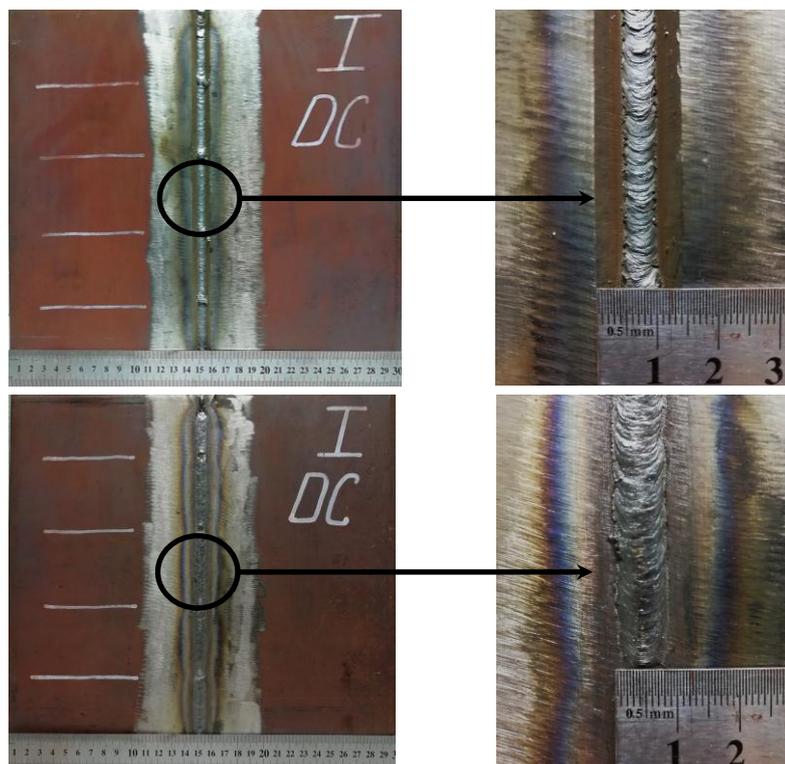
Лицевая сторона и обратный валик сварного соединения, выполненного на постоянном токе обратной полярности
